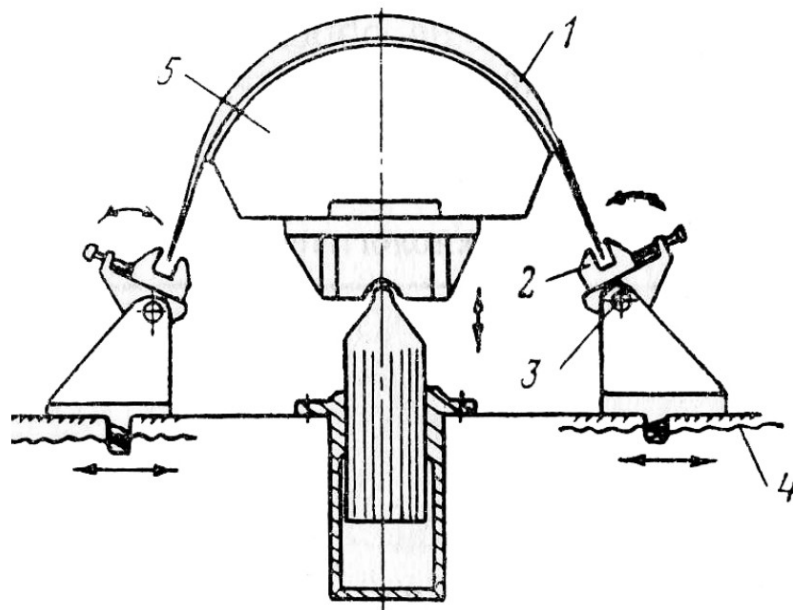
Схема обтяжного пресу типу ОП-3
